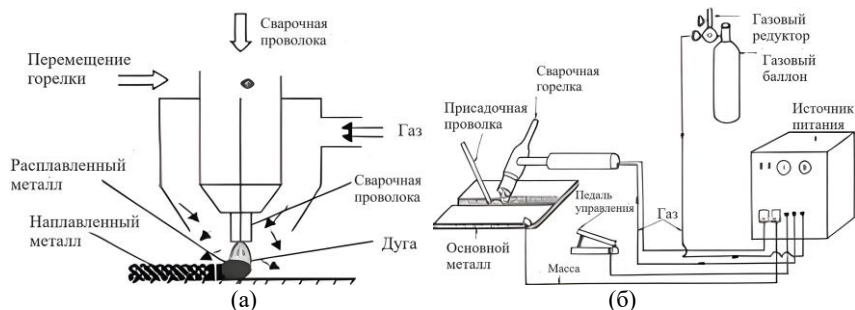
Устройство горелки (а) и оборудование для реализации полуавтоматического сварочного процесса (б)
